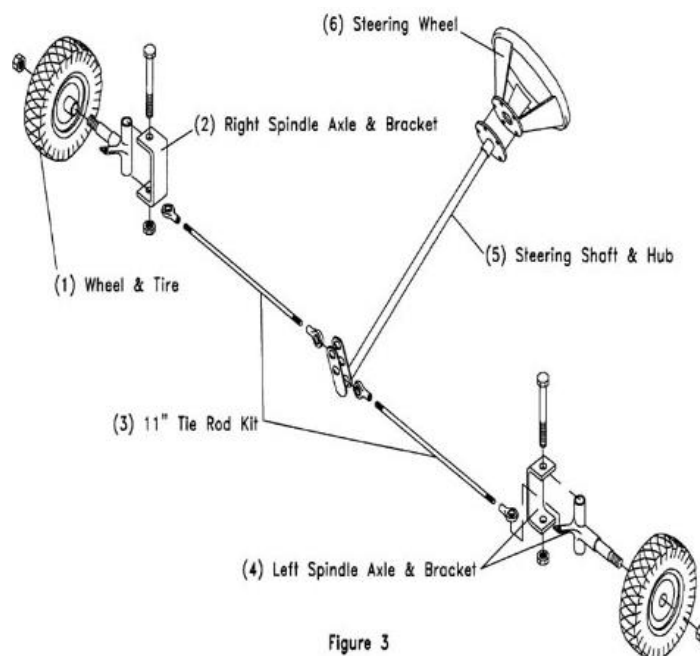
sistema de dirección. Fuente: <https://www.zonagravedad.com>
